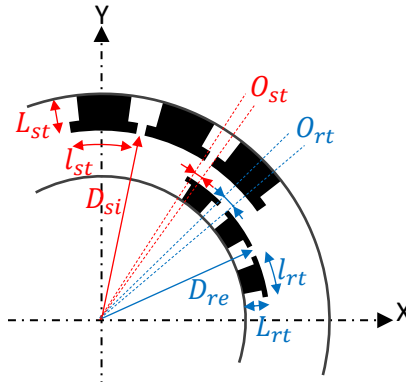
Géométrie des encoches du stator et du rotor
